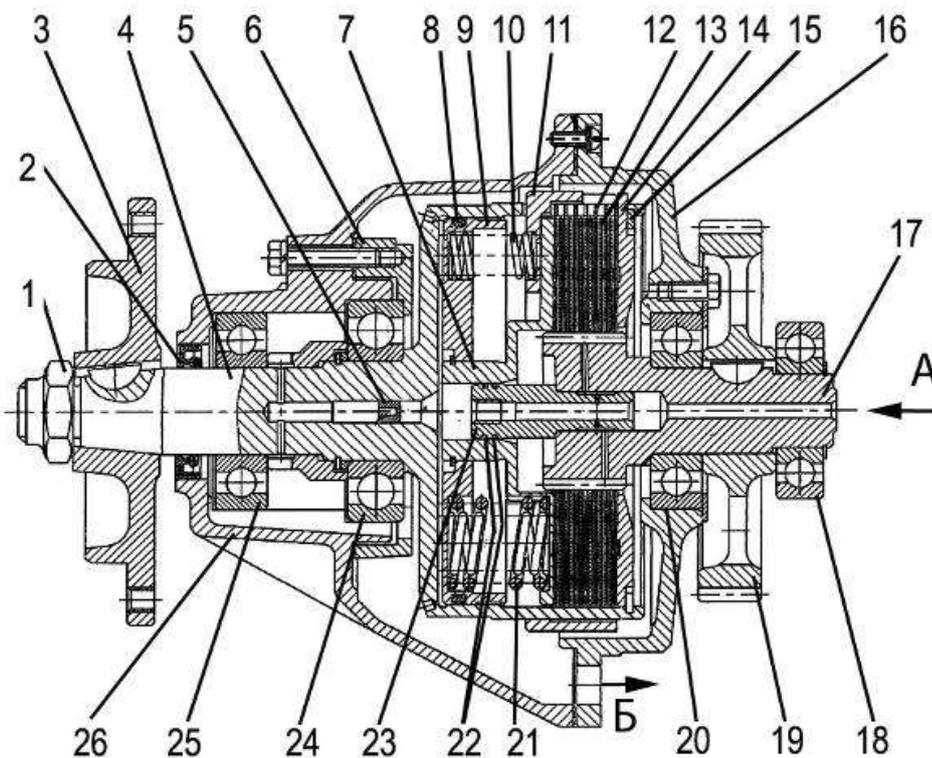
Привод вентилятора двигателя 8525.10:
